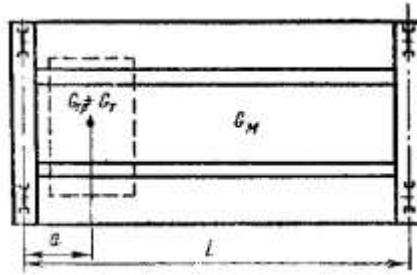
Схема к определению максимальной нагрузки на ходовое колесо мостового крана
